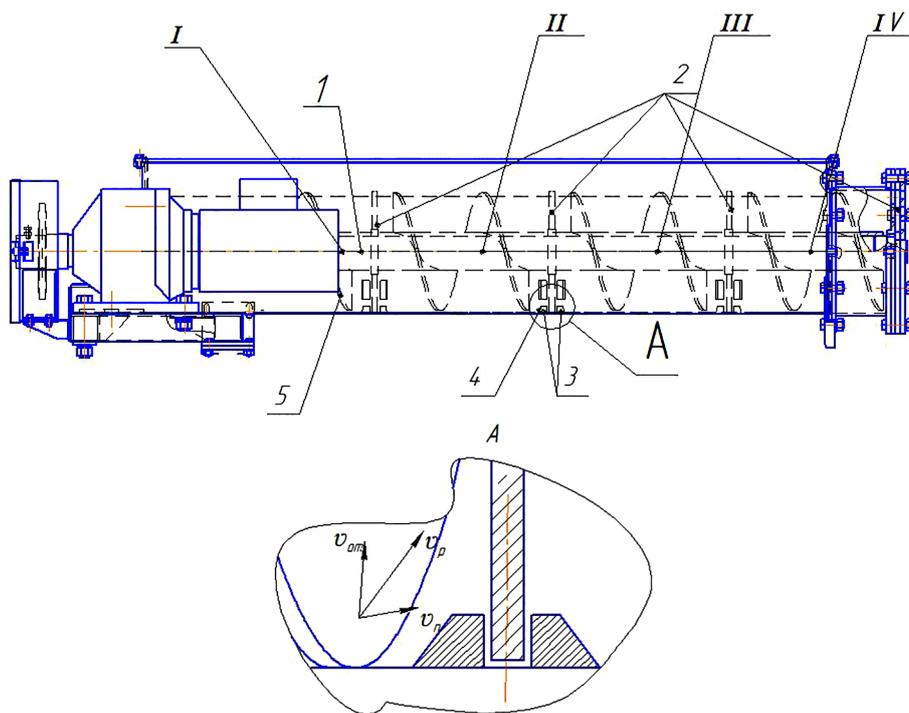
Общий вид измельчителя кормови схема сил, действующих на частицу корма в шнеке: 1 – шнек; 2 – ножи; 3 – противорежущий элемент; 4 – фронтальная грань противорежущего элемента; 5 – навивка шнека
